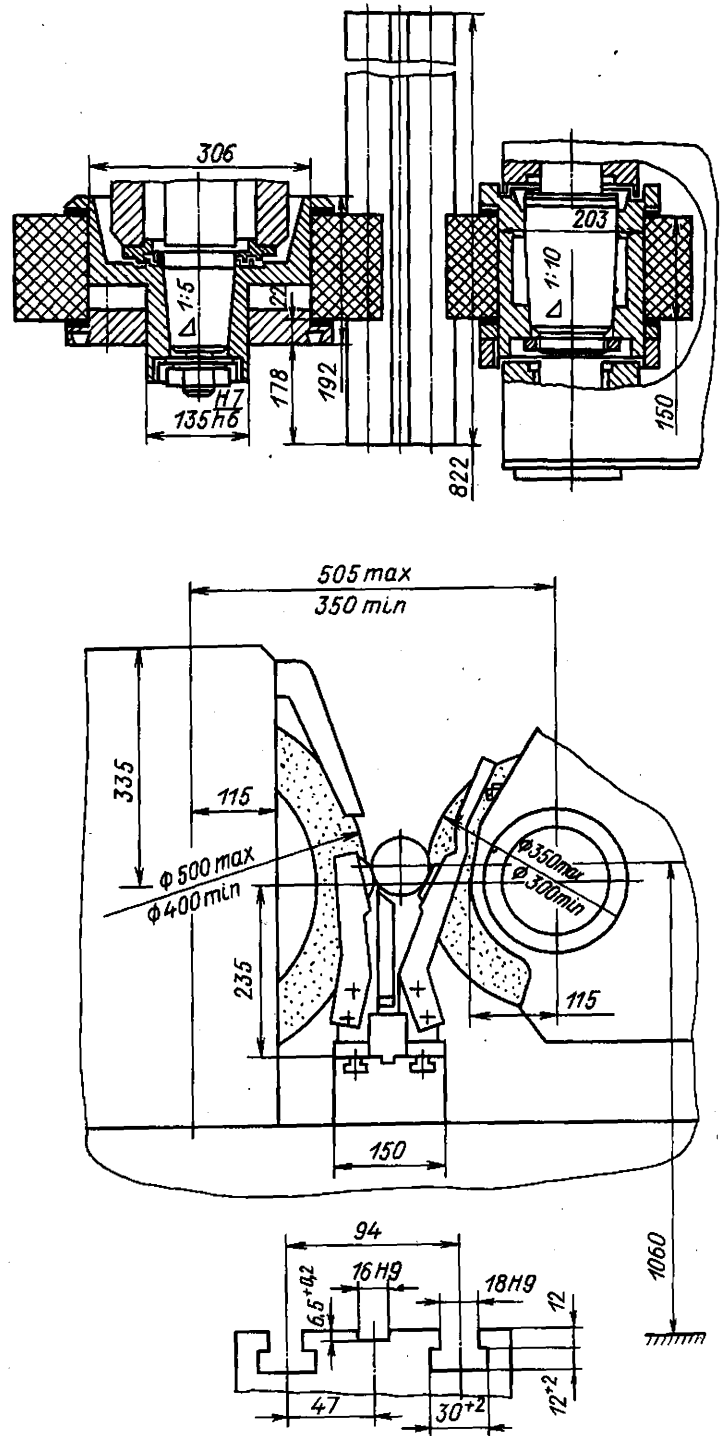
Габаритные размеры рабочей зоны, посадочных и присоединительных баз станка ЗМ184
